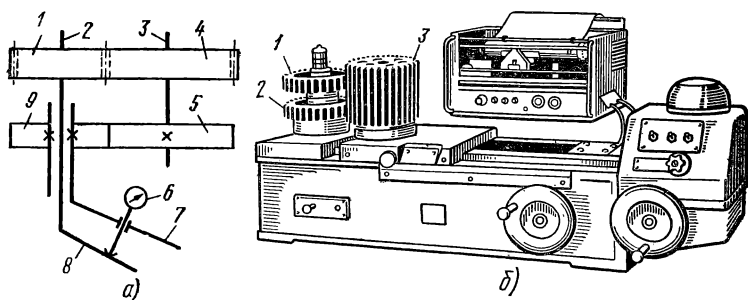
Схема прибора с фрикционными дисками комплексного одно-профильного контроля (*а*) и прибор с промежуточным колесом (*б*)
